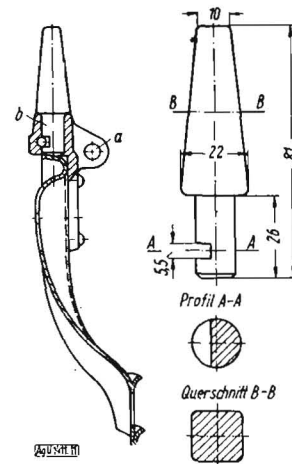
Raufkralle mit flachem Daumen und gelenkiger Befestigung
